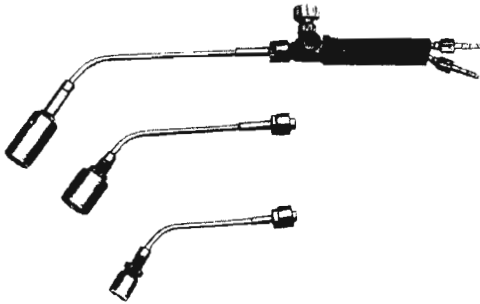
Воздушно-пропановая горелка ГВП-5 для нагрева и пайки
